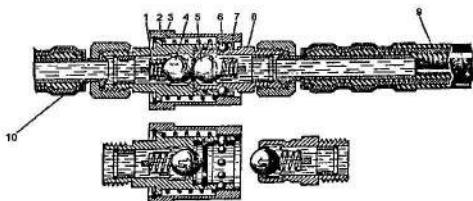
Схема работы быстросоединяемых разрывных муфт Н-052: 1, 3, 7 - пружины; 2 - запорная втулка; 4, 5, 6 - шарики; 8 - корпус; 9 - шланг; 10 - фиксатор шланга.
